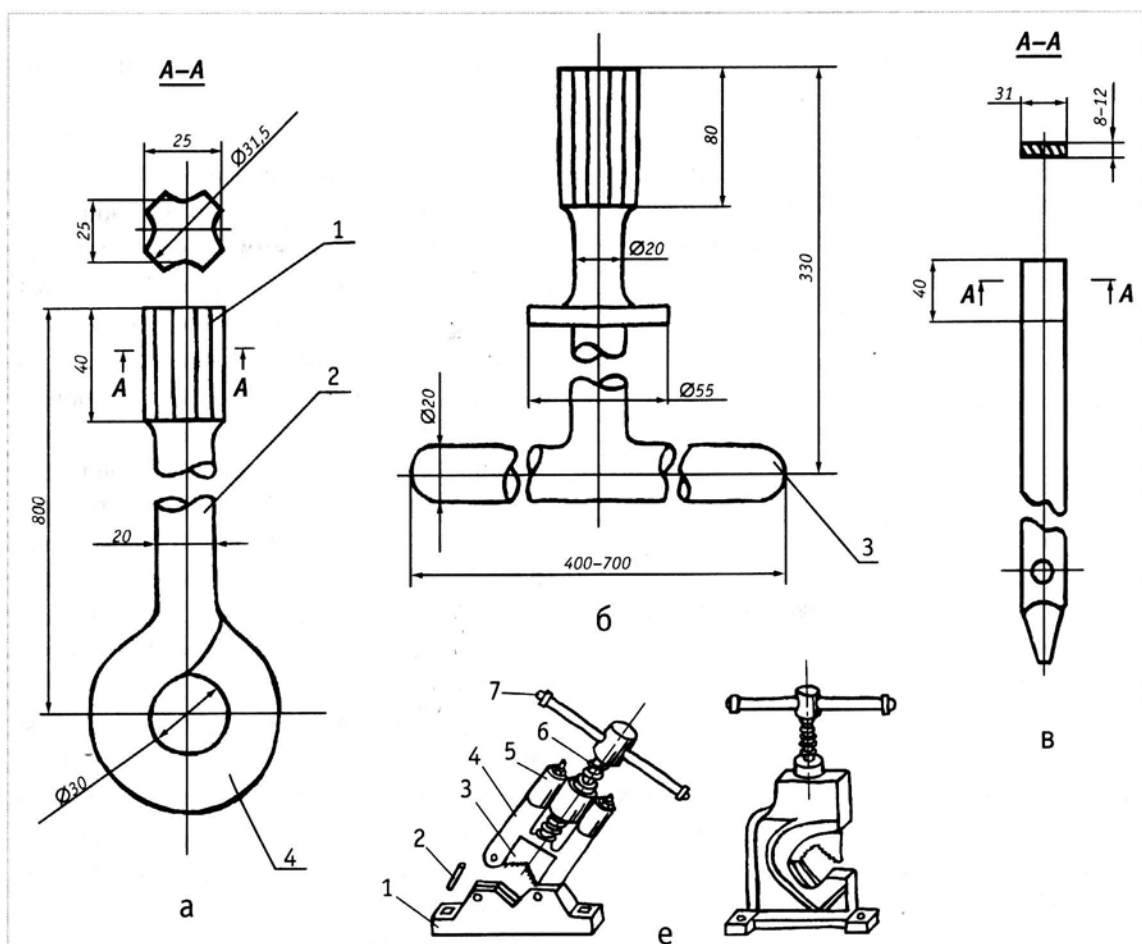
Ключи радиаторные ниппельные: а — длинный ключ для группировки радиаторов; б — короткий ключ для группировки секций; в — ключ, изготовленный из лома; 1 — наконечник; 2 — остов; 3 — рукоятка; 4 — закругление для рукоятки
